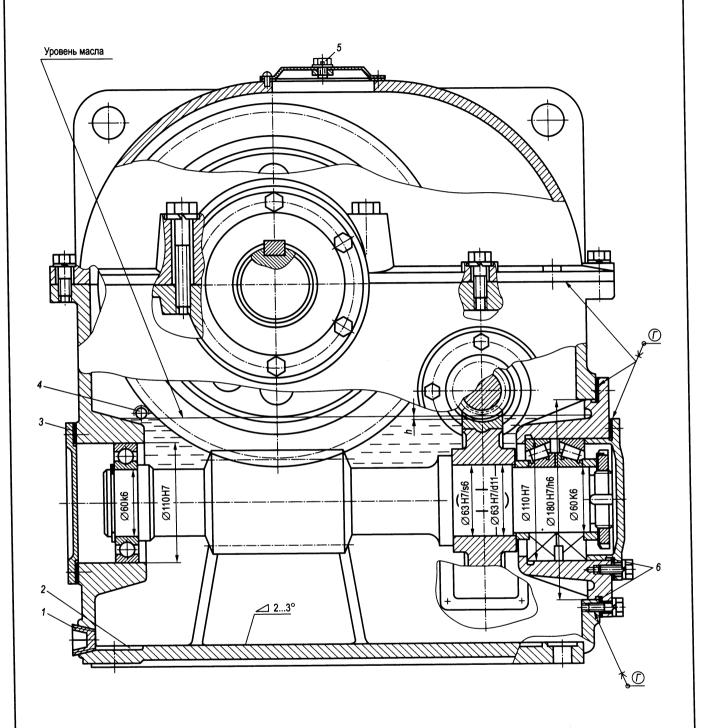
Двухступенчатый червячный редуктор с погружением быстроходного червяка в масляную ванну на глубину h = (1...2) m: 1 – сливная пробка; 2 – приямок; 3 – резиновая плоская прокладка; 4 – контрольная пробка; 5 – заливная пробка-отдушина;
